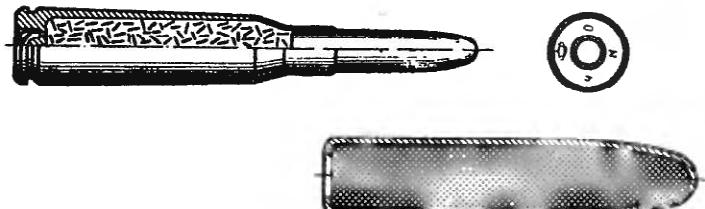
6,5-мм шведский винтовочный патрон с тупоконечной пулей
